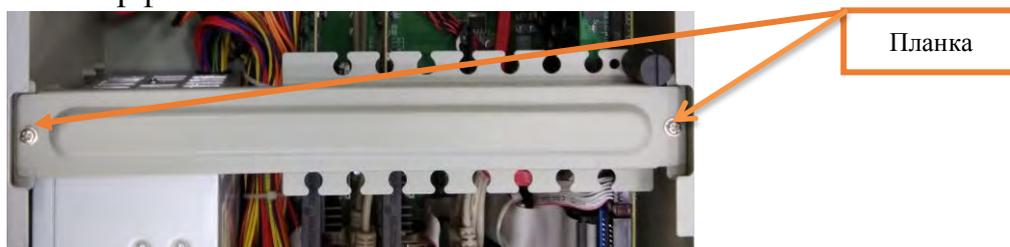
Планка дополнительного крепления плат и блока питания.
